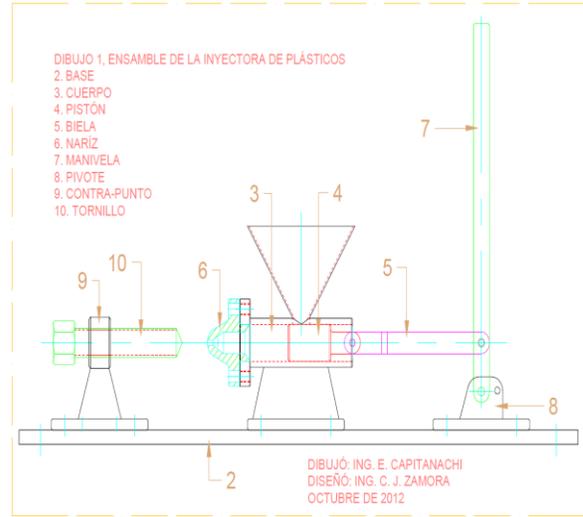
Dibujo del ensamble de la maquina inyectora/extrusora
